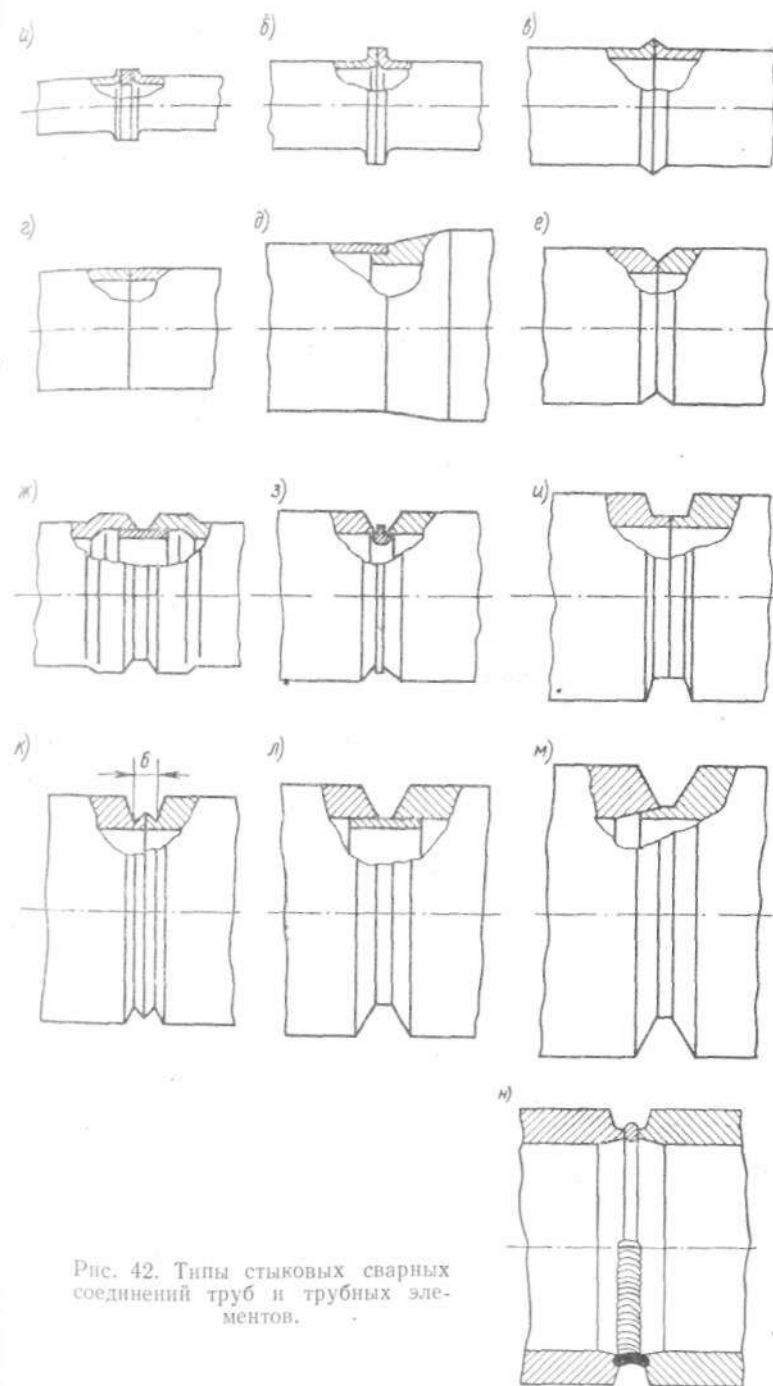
Типы стыковых сварных соединений труб и трубных элементов.
